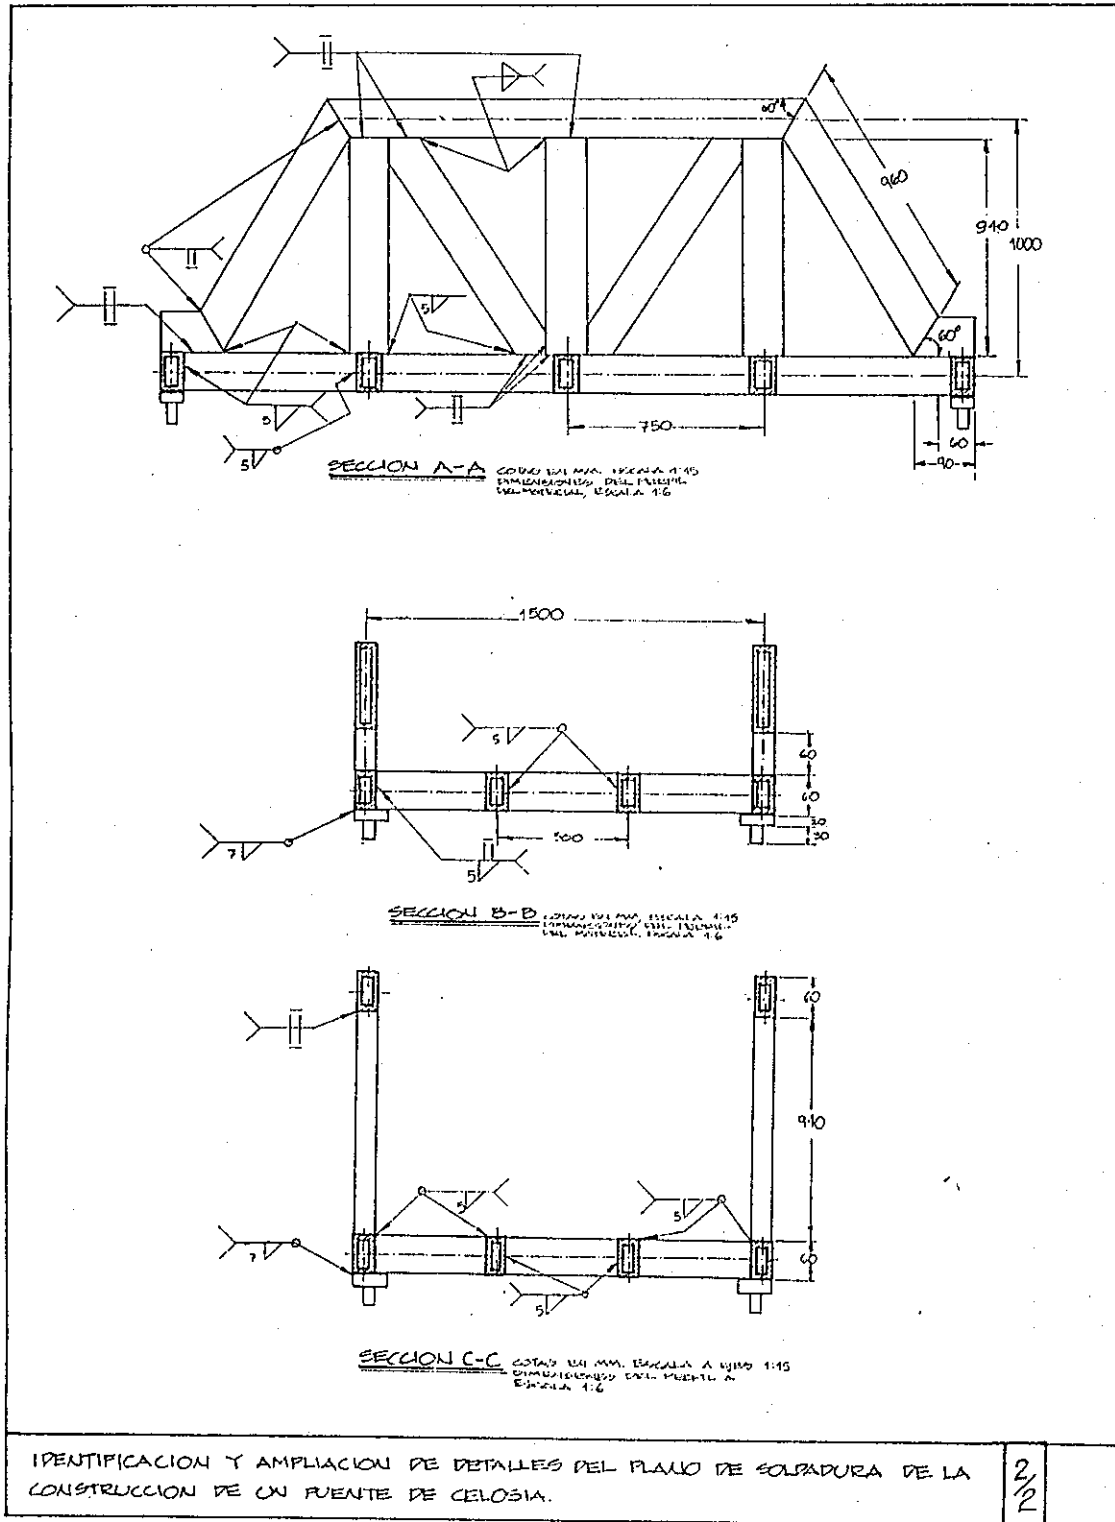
Detalles del plano de soldadura de la construcción de un puente de celosía
